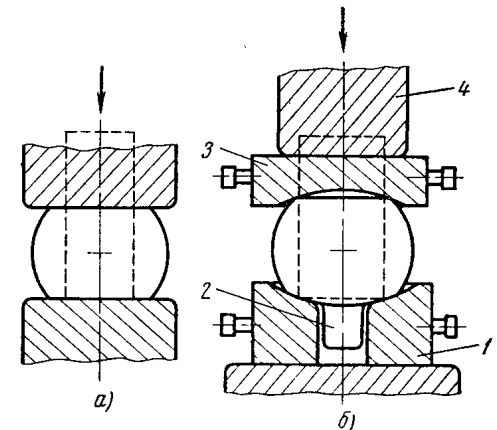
Схема осадки слитков и крупных заготовок под прессом:
